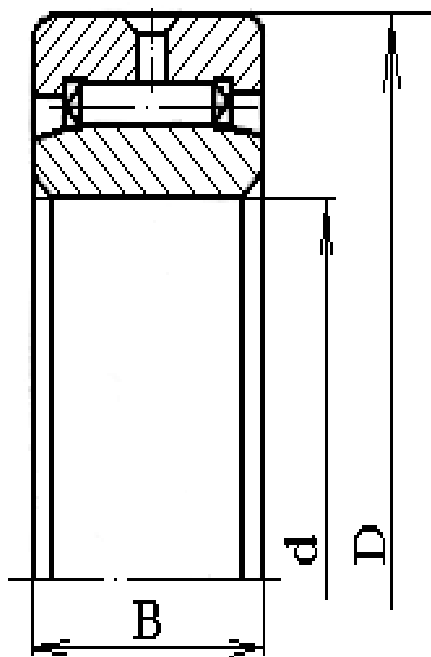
В.5 – Подшипник с длинными цилиндрическими роликами
